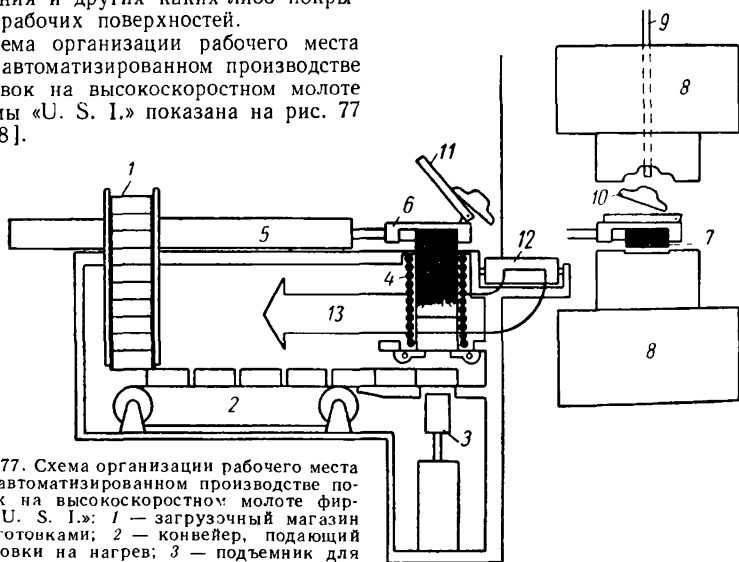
Схема организации рабочего места при автоматизированном производстве поковок на высокоскоростном молоте фирмы «U. S. I.»: 1 — загрузочный магазин с заготовками; 2 — конвейер, подающий заготовки на нагрев; 3 — подъемник для подачи заготовок в индуктор и для проталкивания их через индуктор; 4 — индуктор; 5 — механизм для подачи нагретых заготовок в штамп и отбора отштампованных поковок; 6 — клещи; 7 — нагретая заготовка; 8 — молот для высокоскоростной штамповки; 9 — выталкиватель из верхнего штампа; 10 — поковка; 11 — подхватыватель и сбрасыватель поковок; 12 — приемник для поковок; 13 — конвейер для отбора поковок
